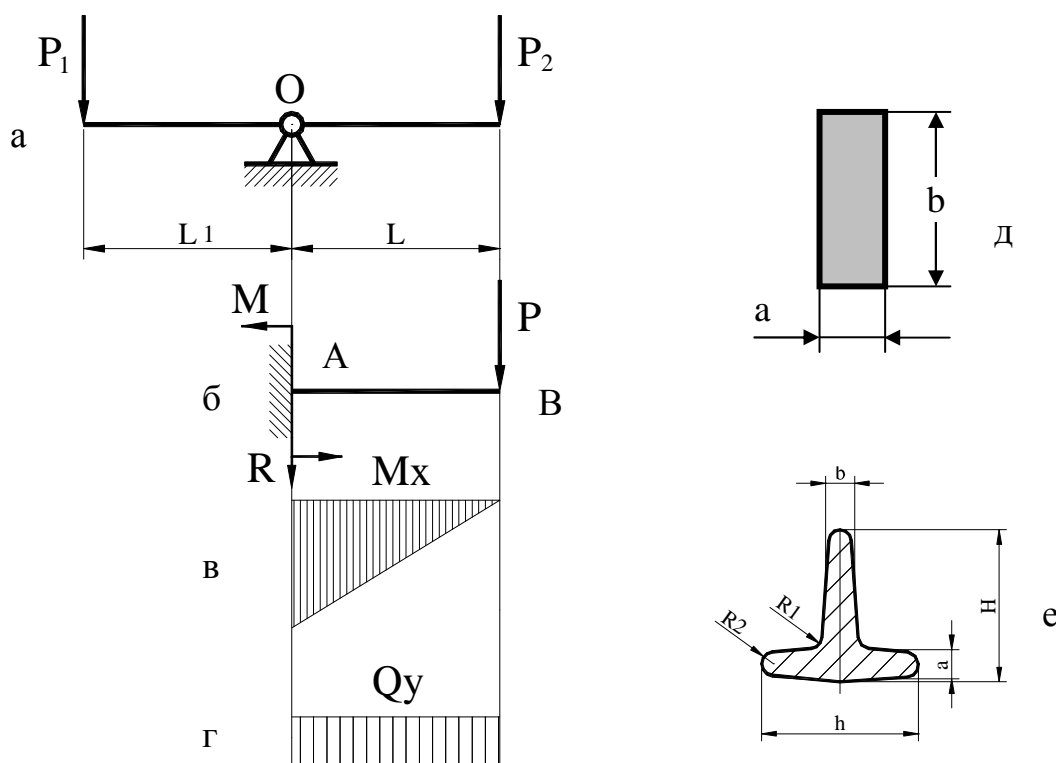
Розрахункова схема: а – схема важеля; б – заміна важеля на защемлену балку; в – епюра згинаючих моментів; г – епюра поперечних сил; д – прямокутний поперечний переріз важеля; е – тавровий поперечний переріз важеля
